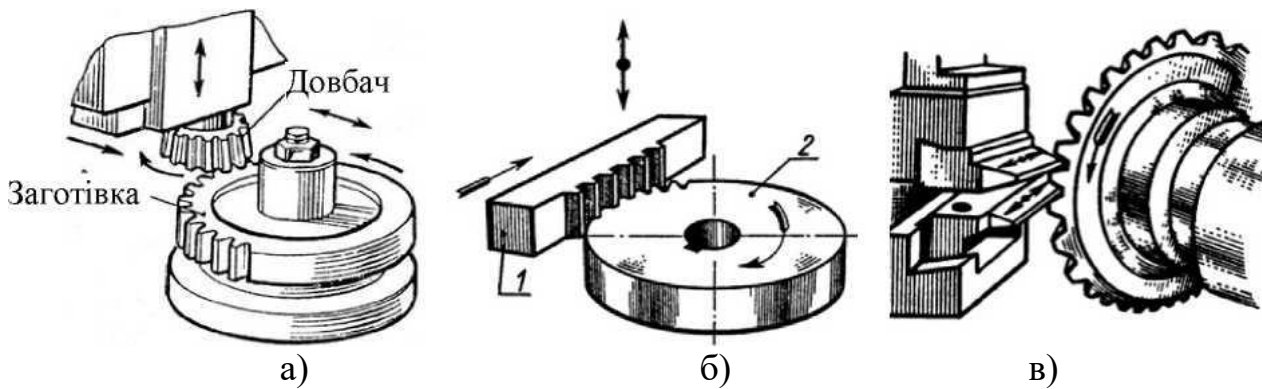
Нарізання зубів: а – довбачем; б – рейкою; в – різцями
